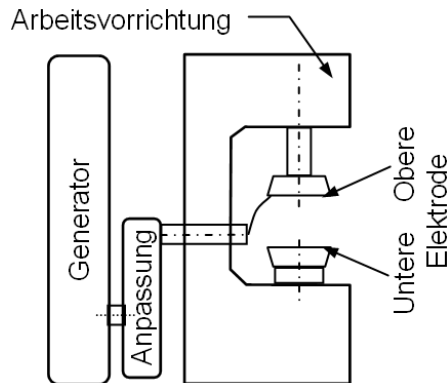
Hochfrequenz-Schweißmaschine.
